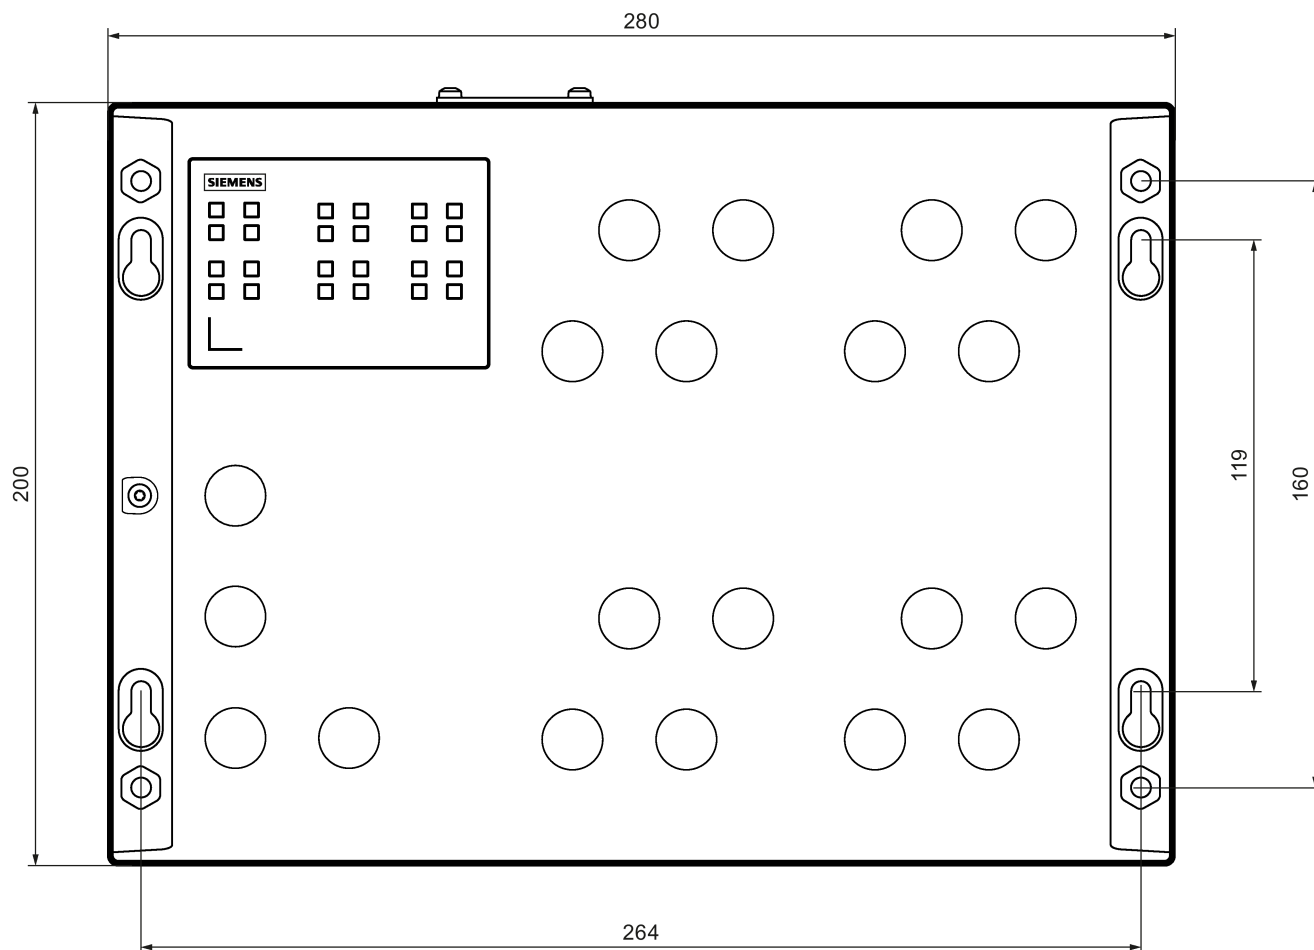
Largeur, hauteur et cotes pour la fixation murale
